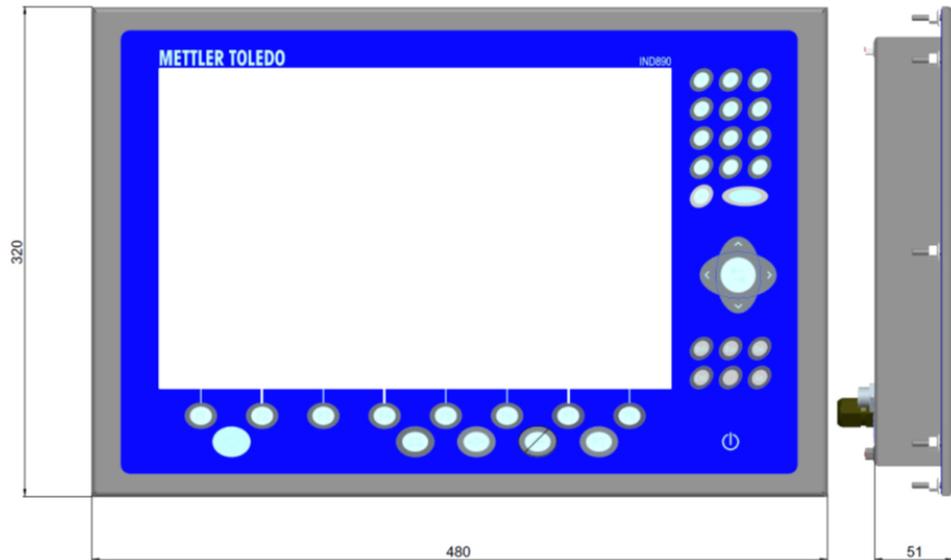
Dimensiones de IND970-15 para el montaje en cuadro de control
